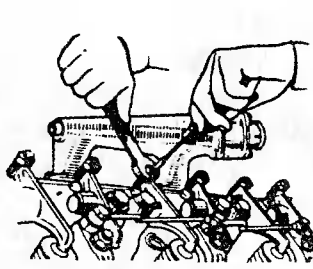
Отвертывание контргайки регулировочного винта
